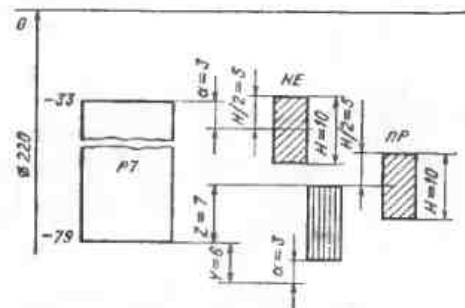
Схема расположения полей допусков калибров для размера 220P7
